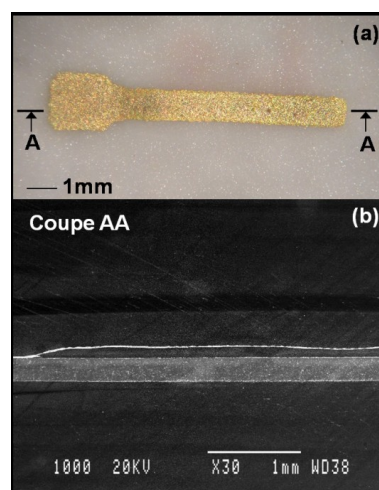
Photo et coupe MEB d'une poutre sérigraphiée en or [40]
